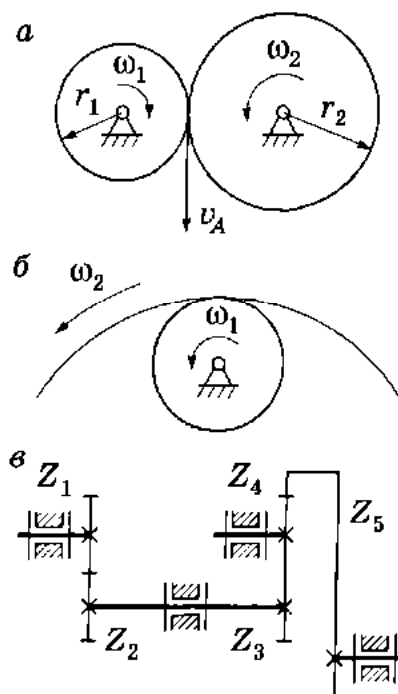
Зубчатая передача зацепления; а — внешнего; б — внутреннего зацепления; в — рядовой зубчатый механизм
